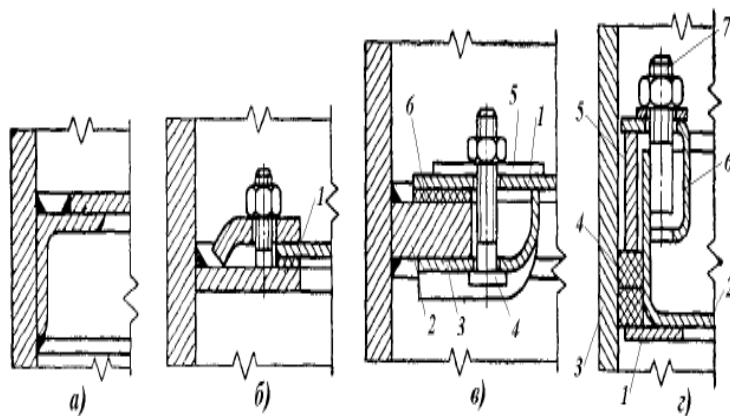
Варианты крепления полотна тарелки к корпусу: а – сваркой; б – на прокладке с прижимной планкой сверху; в – на прокладке со струбциной; г – на сальнике с набивкой.
